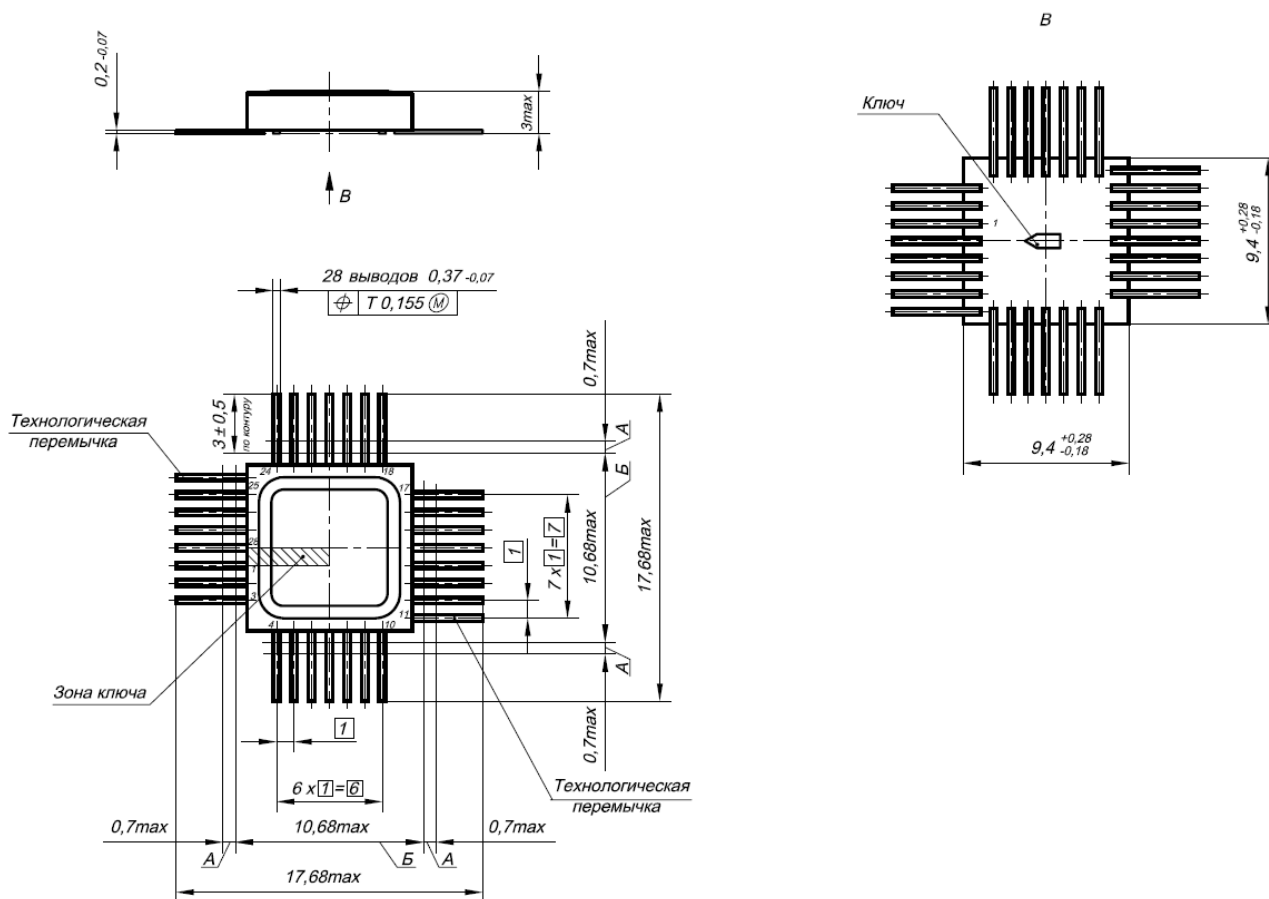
Габаритный чертёж микросхемы 1583HA065 в корпусе H09.28-1B
